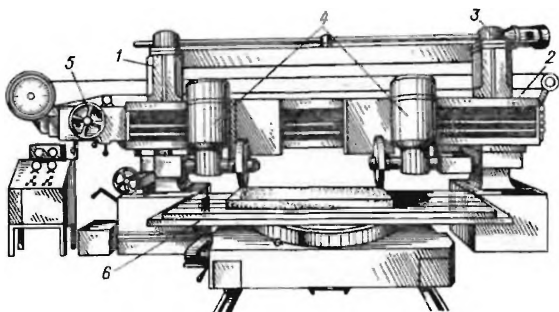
Фрезерно-окантовочный порталный станок модели МП-600 фирмы «Карл Майер»
